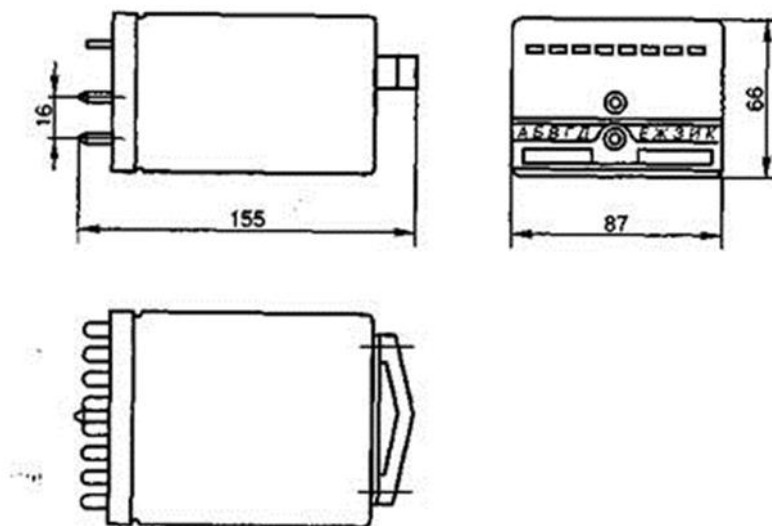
Габаритный чертеж реле типов РНМ1, РНМЗ, РНМЗ-У
